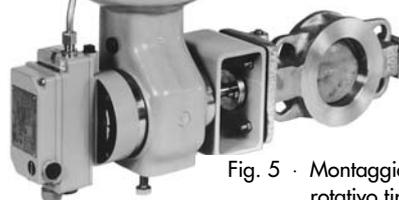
· Montaggio su attuatore rotativo tipo 3278
